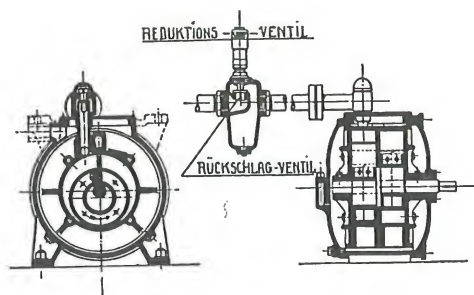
Elektrisch angetriebene Luftsaugepumpe der selbsttätigen Vakuumbremse.
